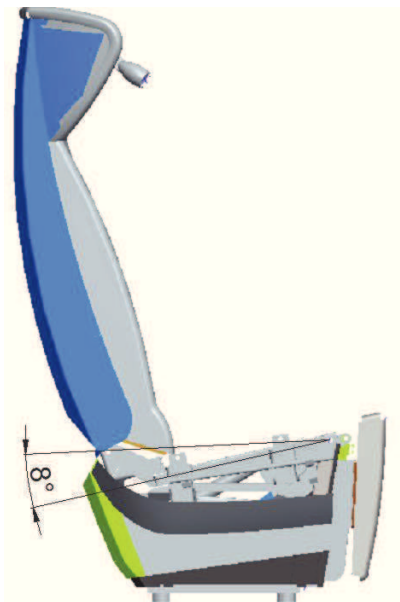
Uložení původního motoru v sestavě (boční pohled)
